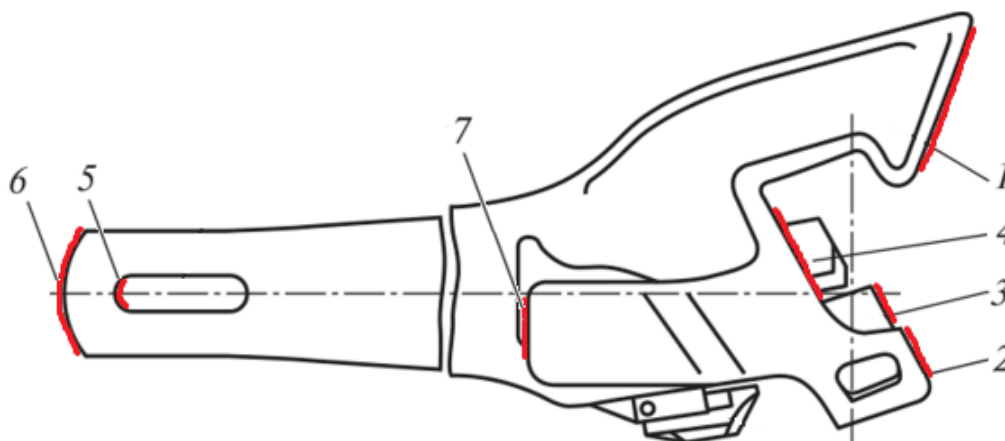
Зоны контакта при сжатии (сцепление, торможение)
